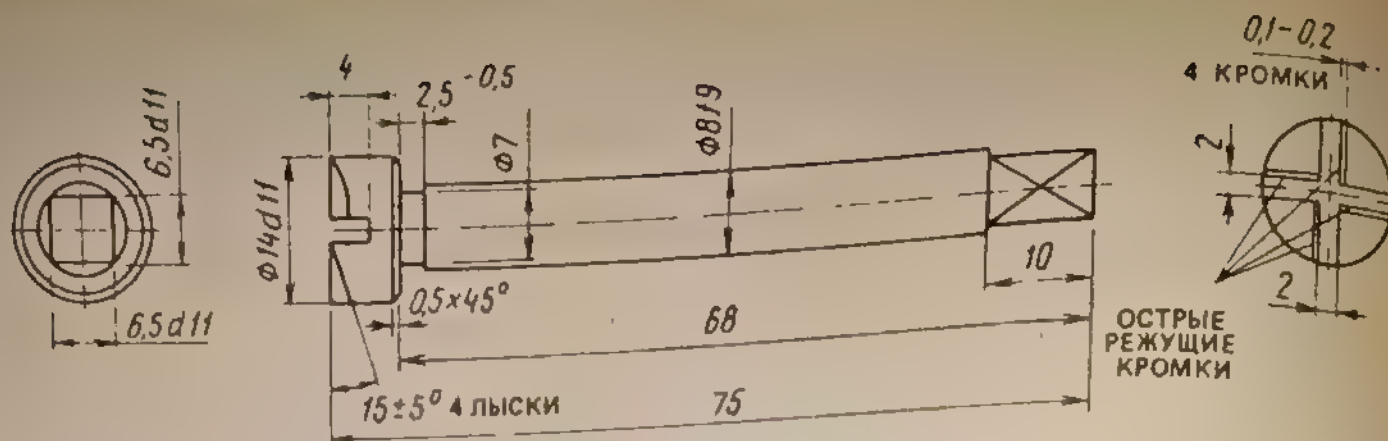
Фреза для доработки ножеобразного седла в корпусе поплавкового клапана противодавления
